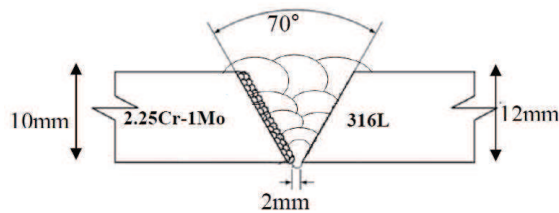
Détails sur le joint soudé [SHA 10]
